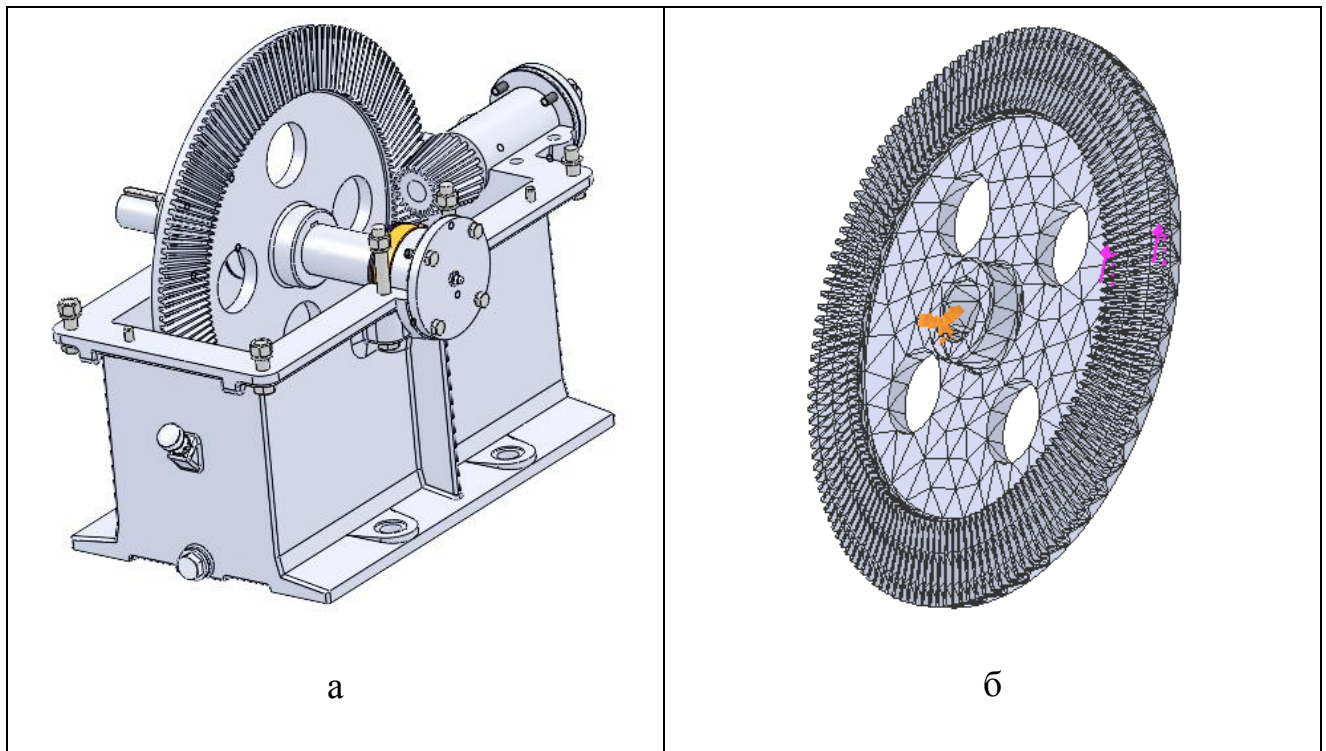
Твердотільна модель редуктора (а) і скінченно-елементна модель конічного колеса
